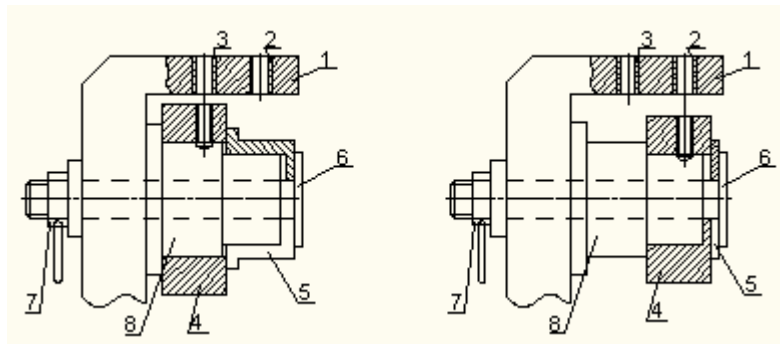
Кондуктор для сверления отверстий в деталях двух типоразмеров. 1 – корпус приспособления, 2, 3 – кондукторные втулки, 4 – деталь, 5 – шайба, 6 – шток с резьбой, 7 – гайка, 8 – оправка.
